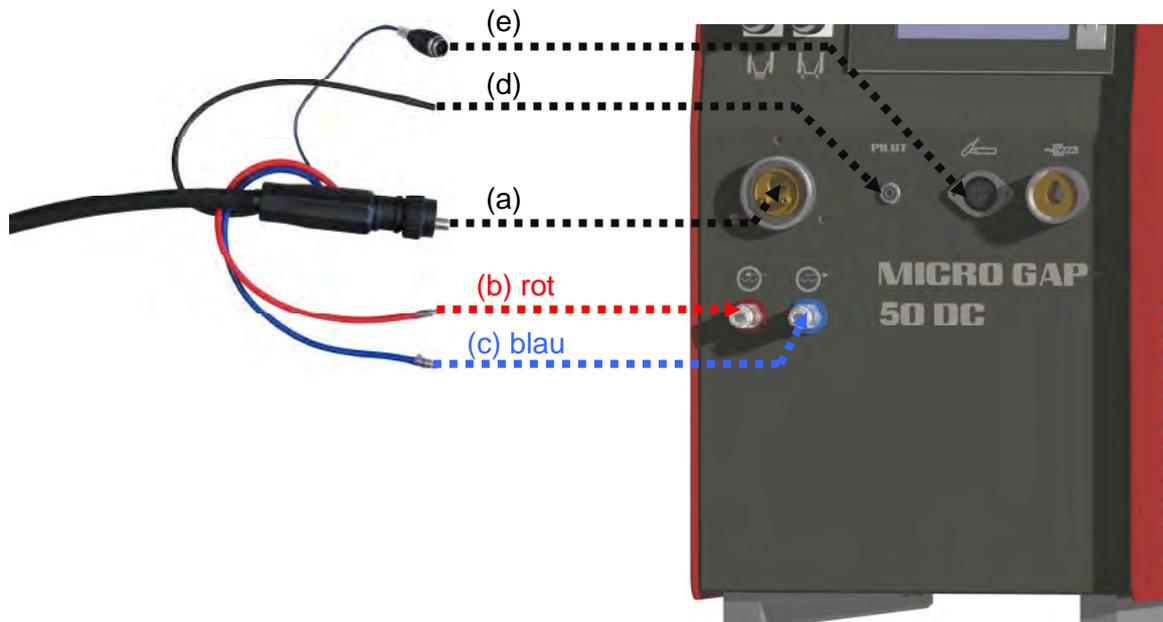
a: Plasma- Hand- Schweißbrenner anschließen
